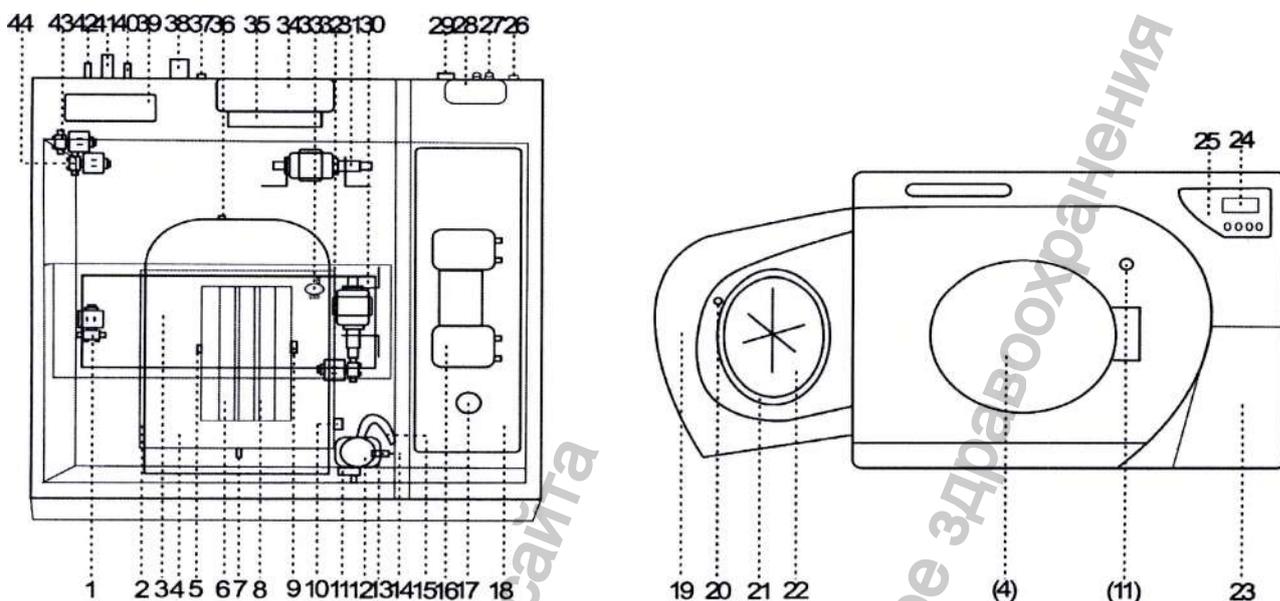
Чертеж Стерилизатора парового T&S23B
